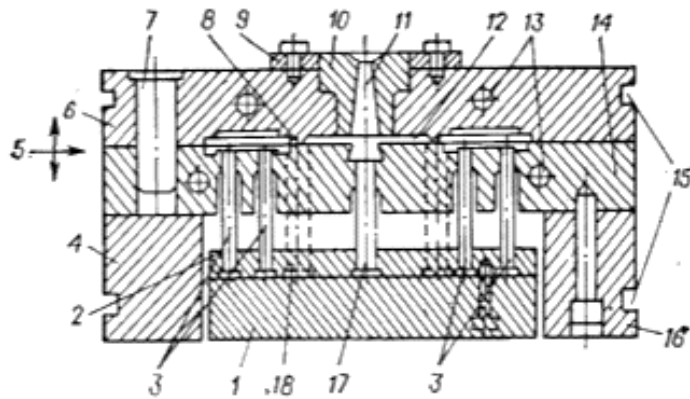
Ливарна форма звичайного типу: 1,2-нижня і верхня з'єднувальні планки системи штовхання; 3 - виштовхувачі; 4,16 - підкладки; 5 - площина роз'єму; 6 - матриця форми; 7 - напрямна колонка; 8 - впуск; 9 - напрямна кільця; 10 - літнікова втулка; 11 - літинковий канал; 12 - канал для розведення; 13 - канал для охолодження; 14 - пуансон; 15 - пази для кріплення; 17 - центральний виштовхувач (виштовхувач ливника); 18 - штифт для зворотного приземлення виштовхувача.
